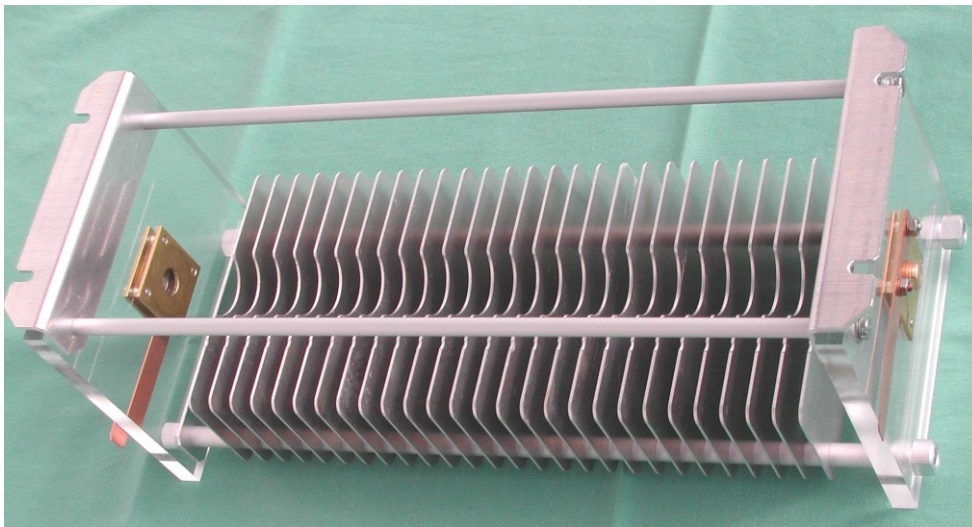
Zusammengebauter Stator mit Plexiglas-Endplatten, Lagerdeckeln und Fußwinkeln
